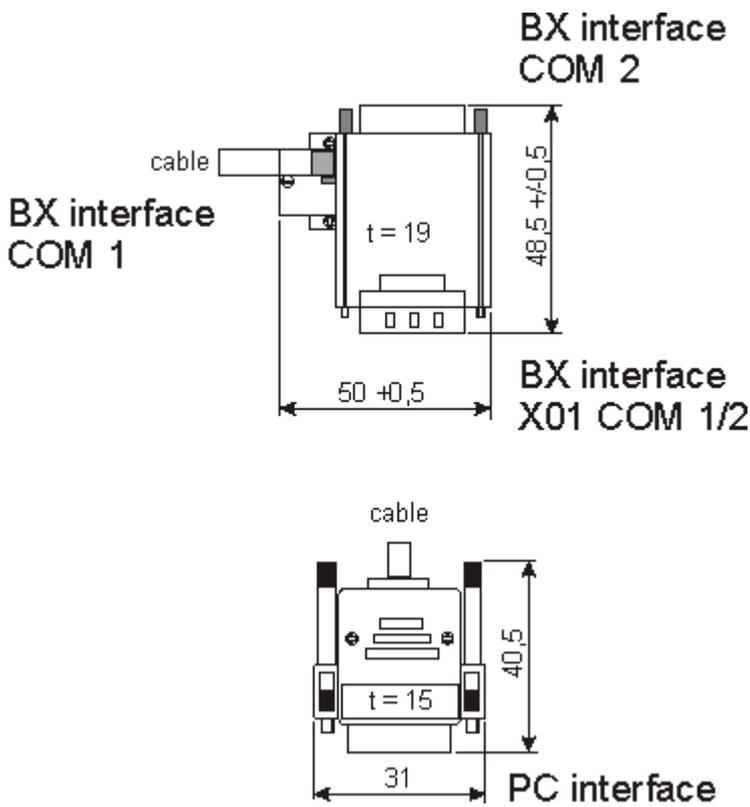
Programmierkabel ZK1000-0030 - Abmessungen der Stecker
